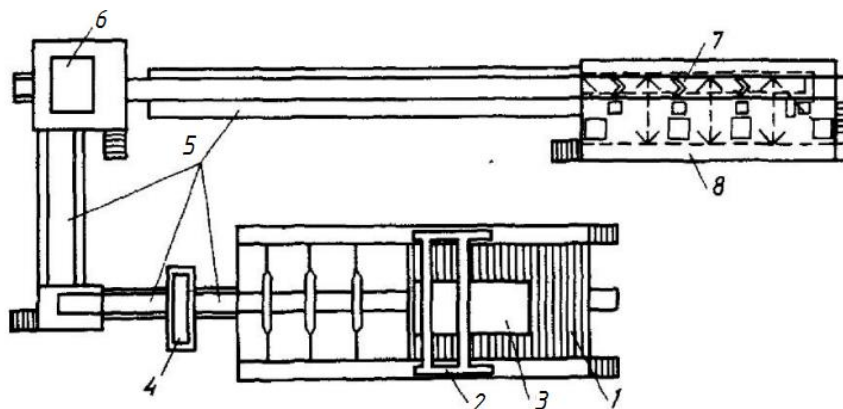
Схема технологической линии по переработке некондиционного железобетона
